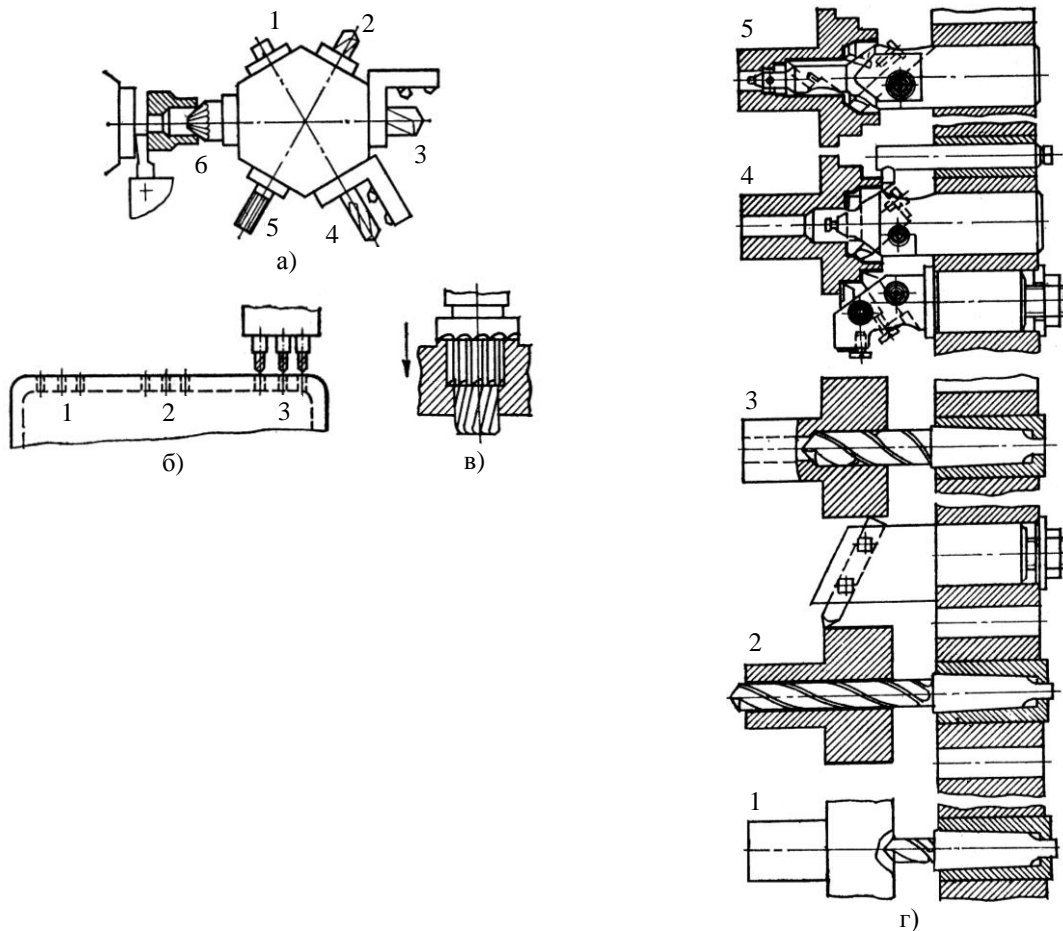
Схема одномісної паралельно-послідовної багатоінструментної обробки:
